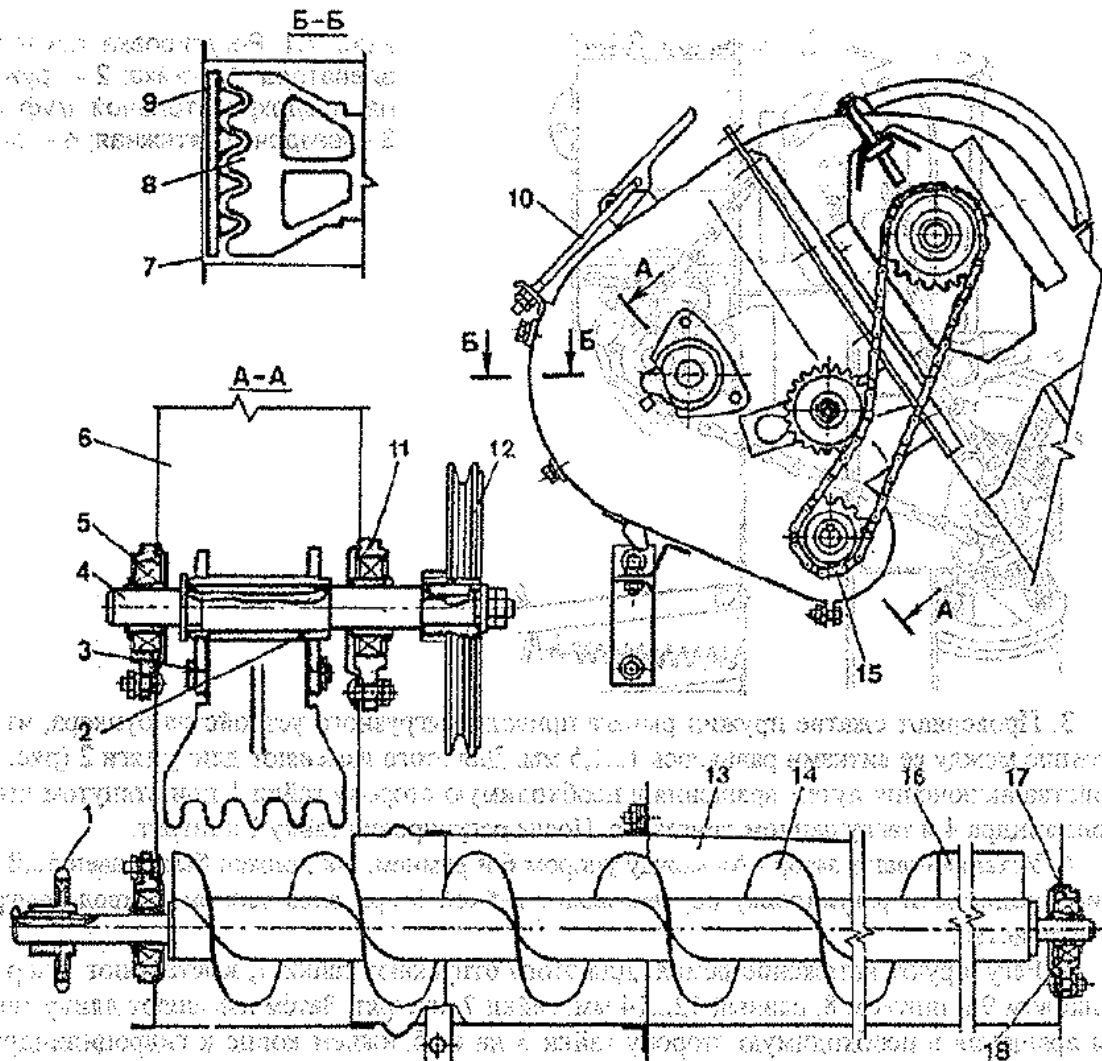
Домолачивающее устройство: 1 - звездочка; 2 - ротор; 3 - ось; 4 - вал; 5 и 18 - подшипники; 6 - корпус; 7 - обечайка; 8 - лопасть; 9 - дека; 10 - замок; 11 и 17 - корпуса подшипников; 12 - шкив; 13 - кожух; 14 - шнек; 15 - цепь; 16 - лопатка
